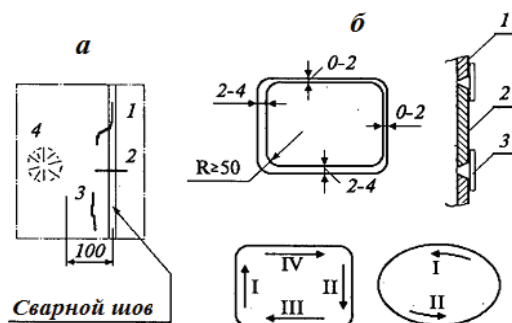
Виды трещин, требующие установки заплат на корпусе (а). Схемы установки и приварки заплат (б):
